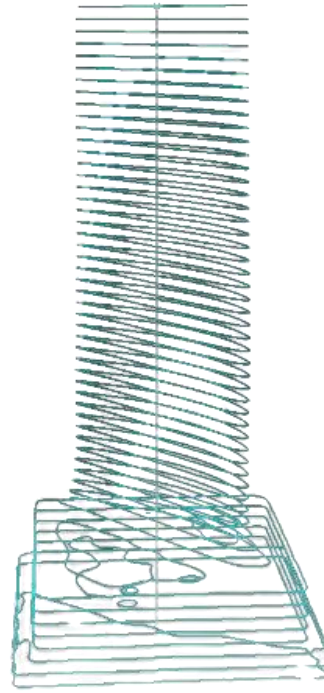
Sections planes sur aube de turbine sans nuage de point et maillage
